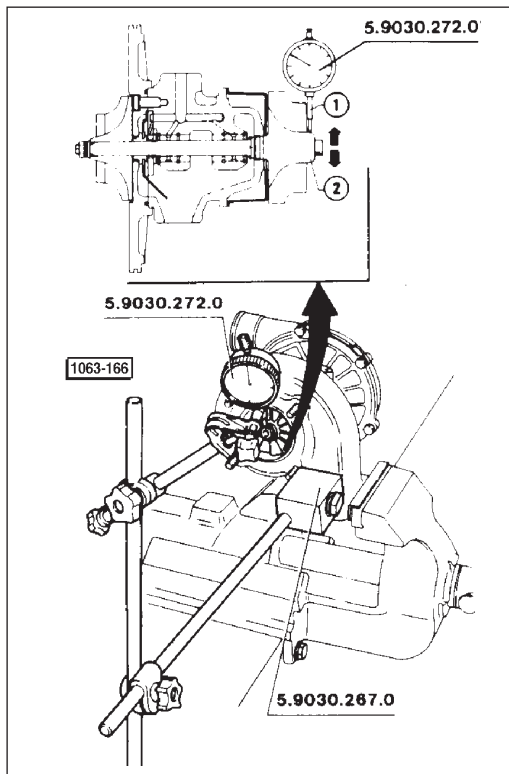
Contrôle du jeu radial de l'arbre rotor.
